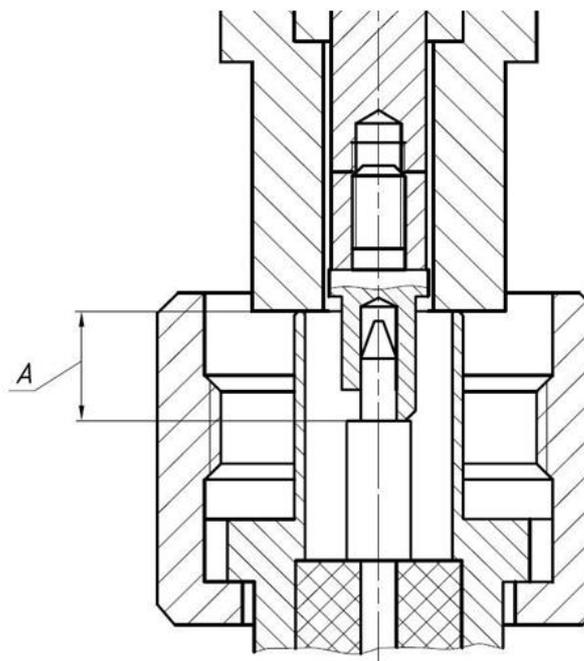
Проверка размера «А» соединителя «вилка»
